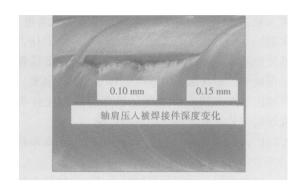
轴肩压入深度由浅到深时焊缝成形变化情况 Fig 7 Formation of weld changed with depth of shoulder
